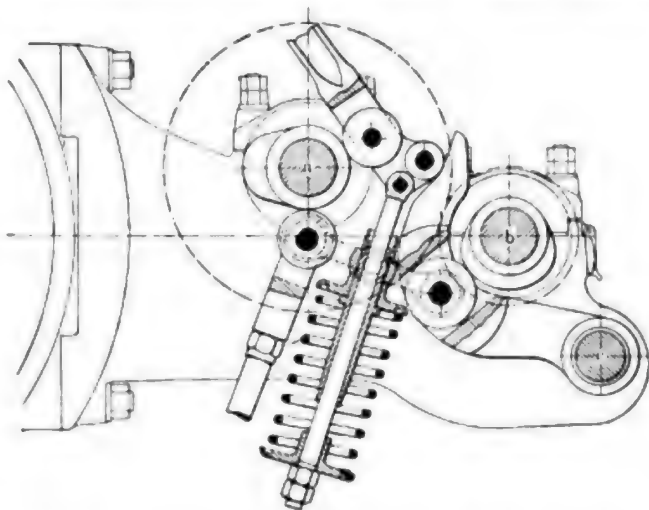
Steuerungsantrieb der Dingerschen Maschinenfabrik, Aktiengesellschaft in Zweibrücken.
